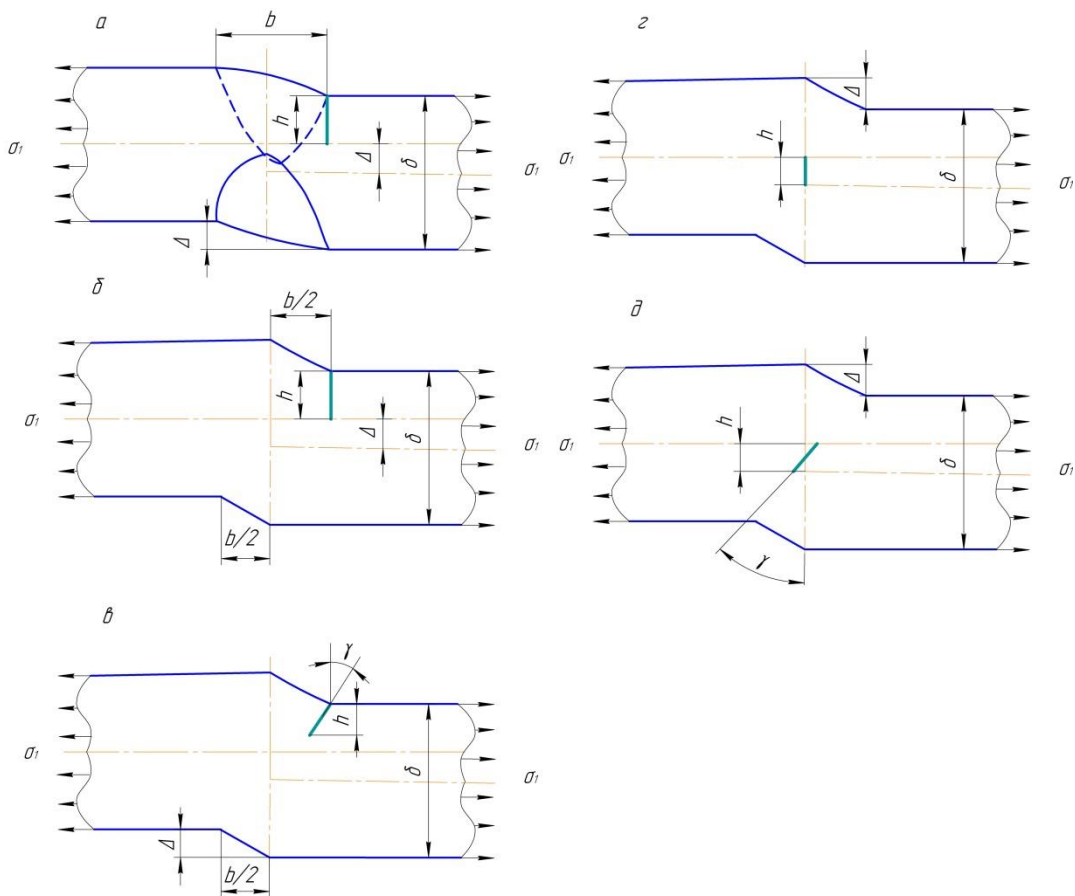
Трещины в сварных двухсторонних стыковых соединениях со смещением кромок.
